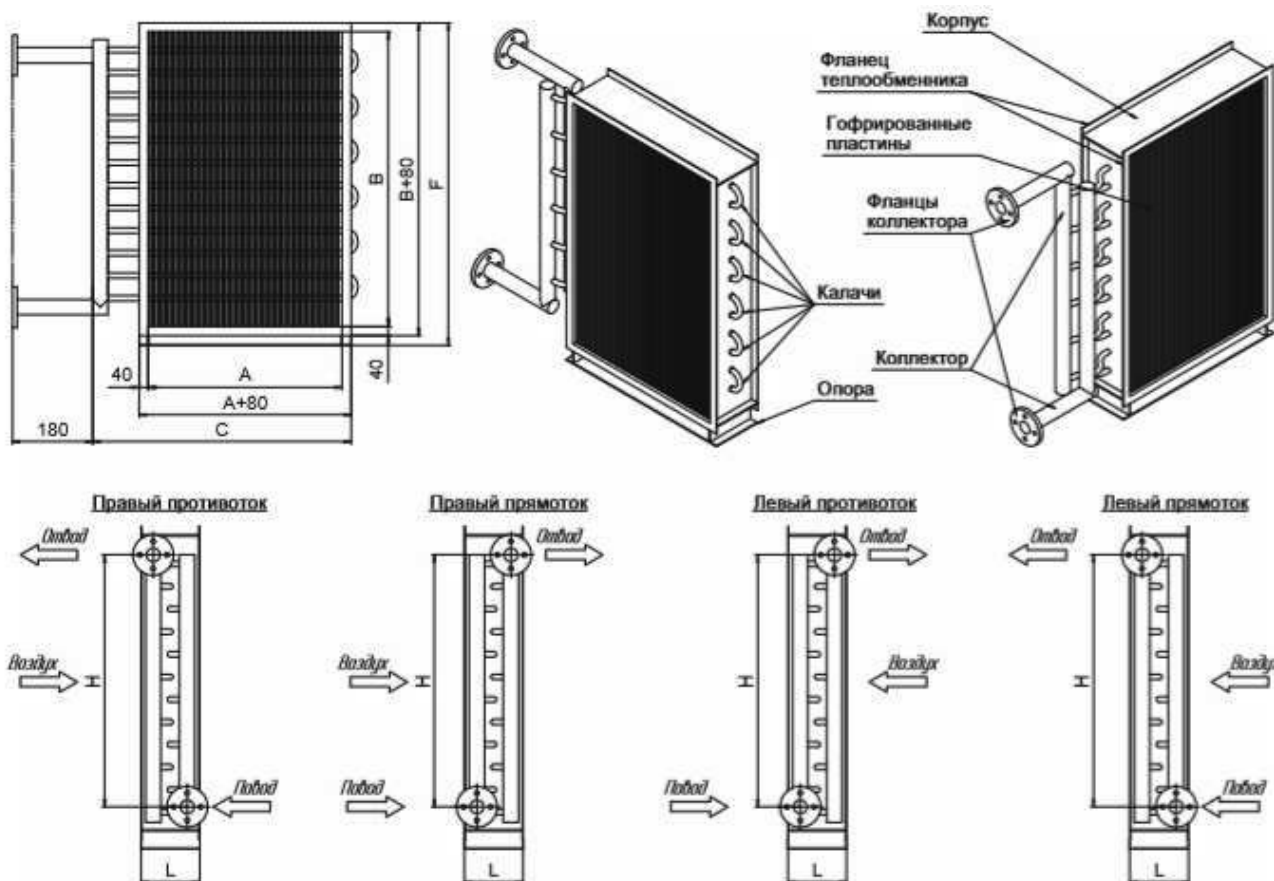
Габаритные размеры двухрядных калориферов
